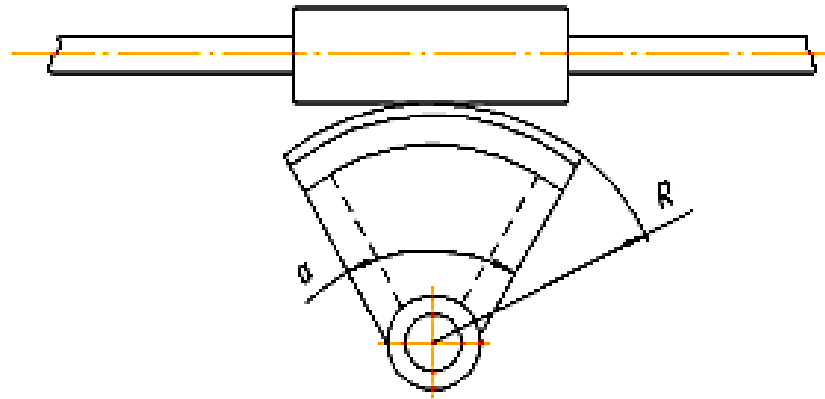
Ручний механізм перемикання швидкостей
